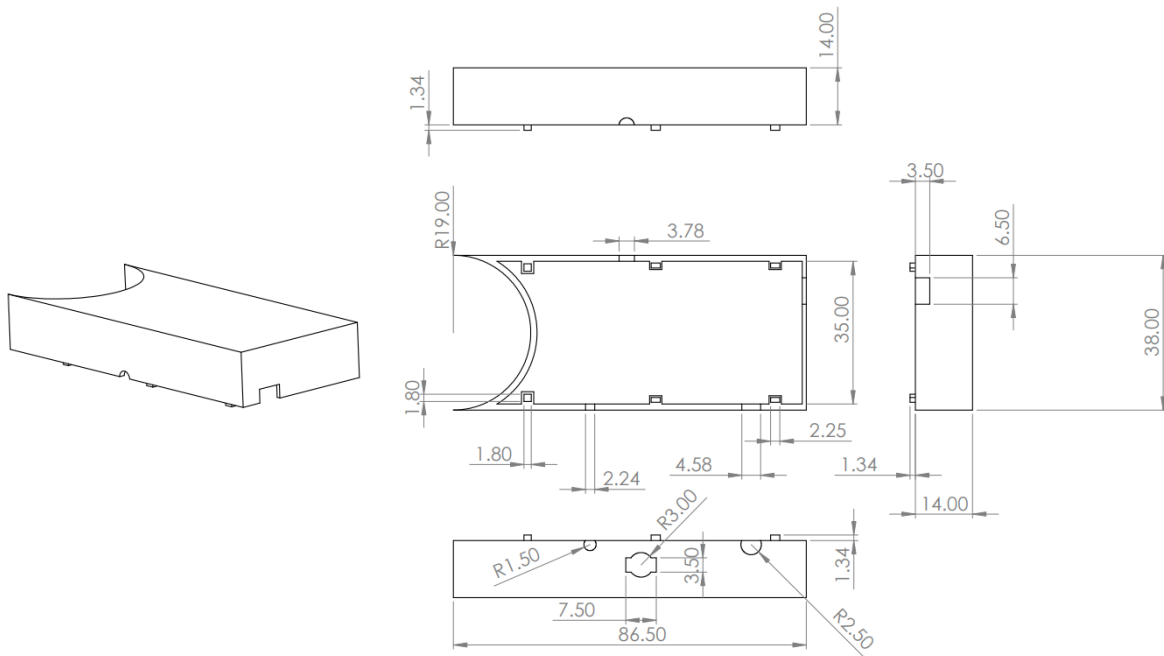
Dimensiones y forma de la pieza superior de la caja para el circuito.
